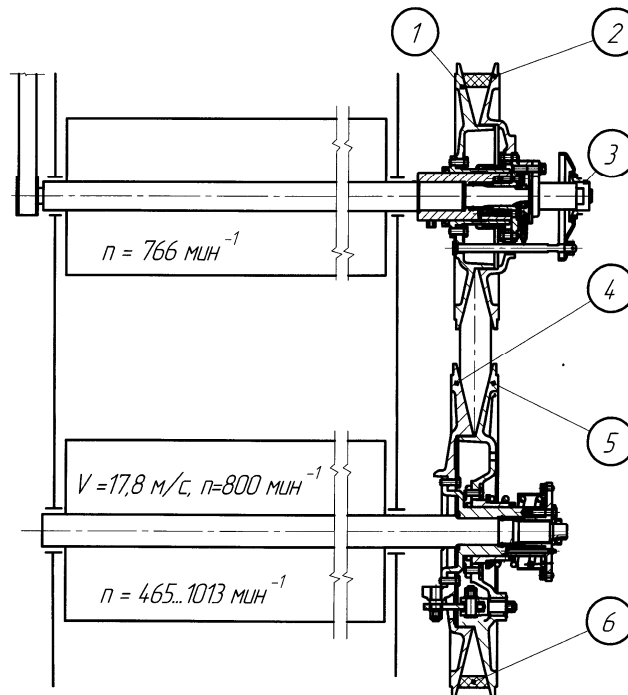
Схема клиноременного вариатора барабана: 1, 2 - подвижный и неподвижный диск ведущего блока; 3 - плунжерный гидроцилиндр; 4, 5 неподвижный и подвижный диски ведомого блока; 6 – ремень
